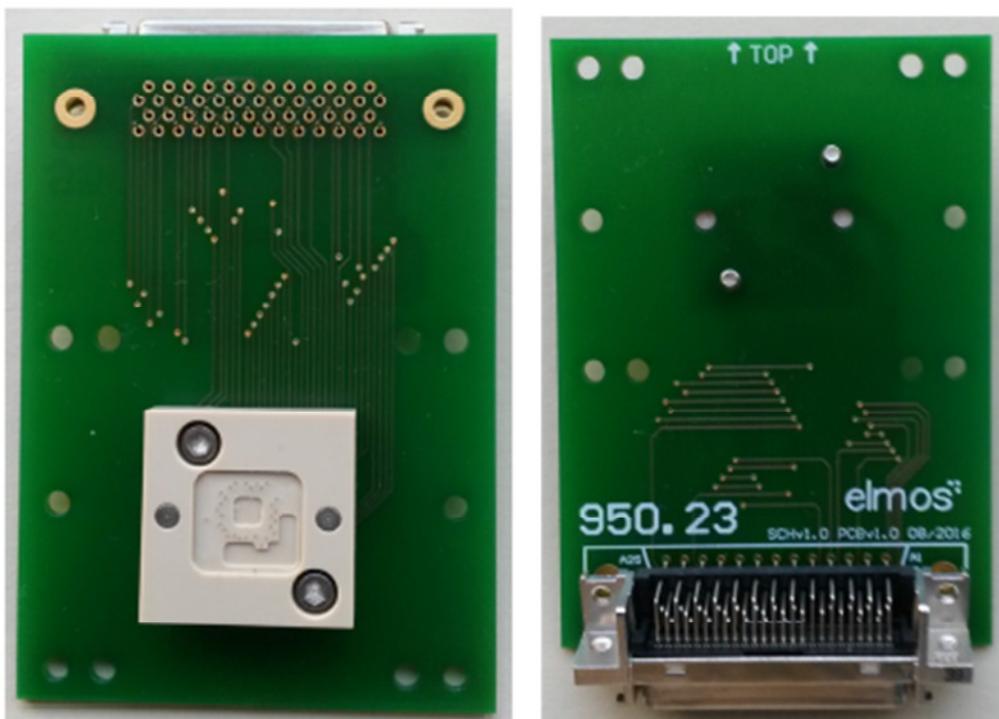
DUT Board zur Verbindung der Kontakteinheit mit der Testmaschine
